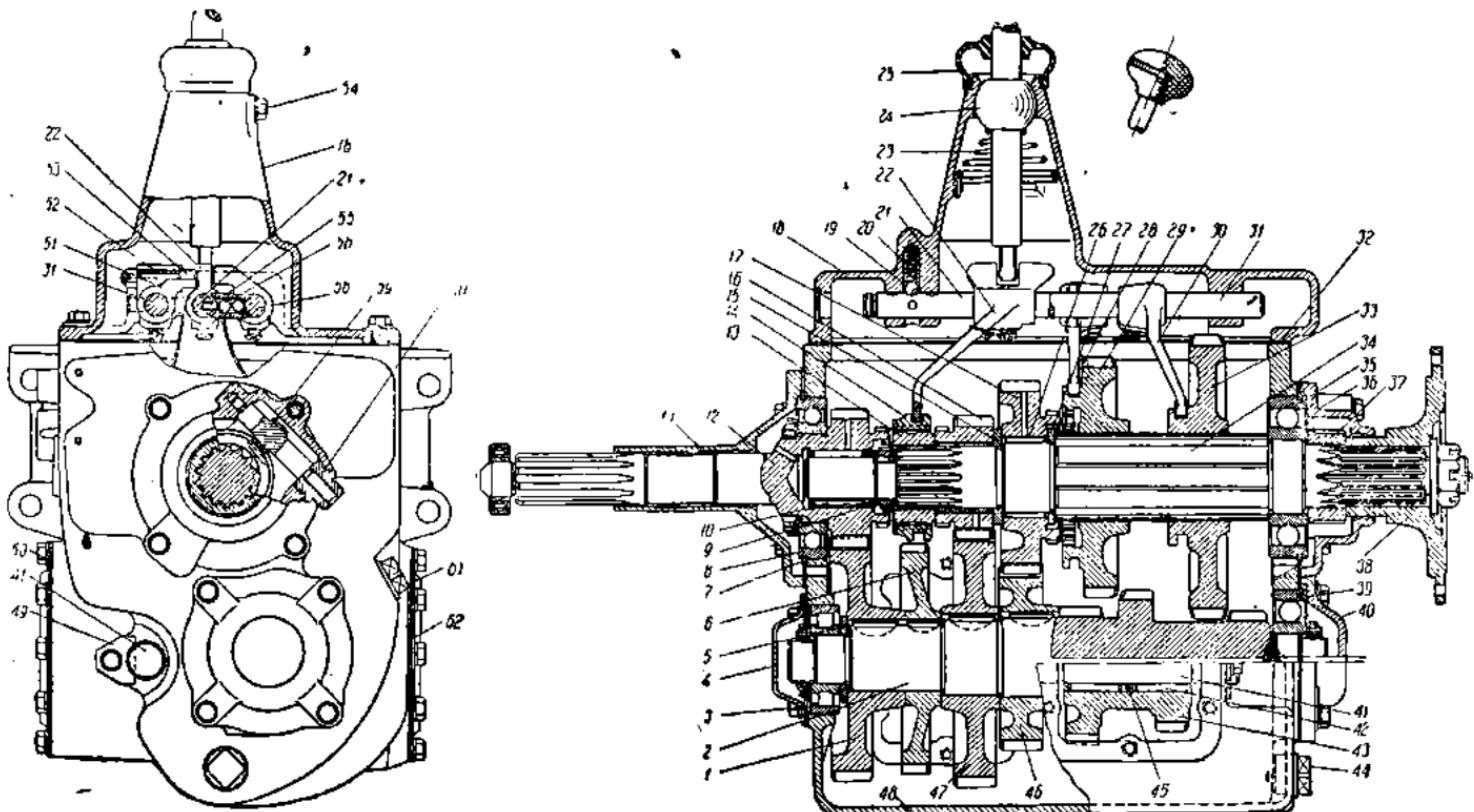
Коробка передач (1 — шестерня постоянного зацепления; 2 — промежуточный вал; 3, 8, 10, 35, 39 и 42 — подшипники; 12 — первичный вал; 13 — муфта включения 4-й и 5-й передач; 16 и 47 — пара шестерен 5-й передачи; 17 и 46 — пара шестерен 3-й передачи; 26 — игольчатый подшипник; 29 — шестерня 2-й передачи; 33 — шестерня 1-й передачи; 34 — вторичный вал; 41 — ось шестерен заднего хода; 43 — блок шестерен заднего хода).
